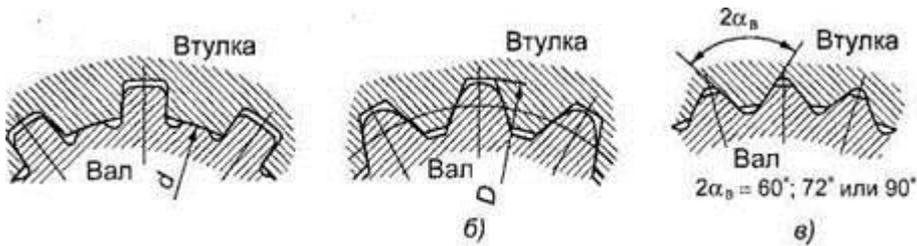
Типы зубчатых (шлицевых) соединений: а — прямоугольные зубья; б — эвольвентные зубья; в — треугольные зубья
